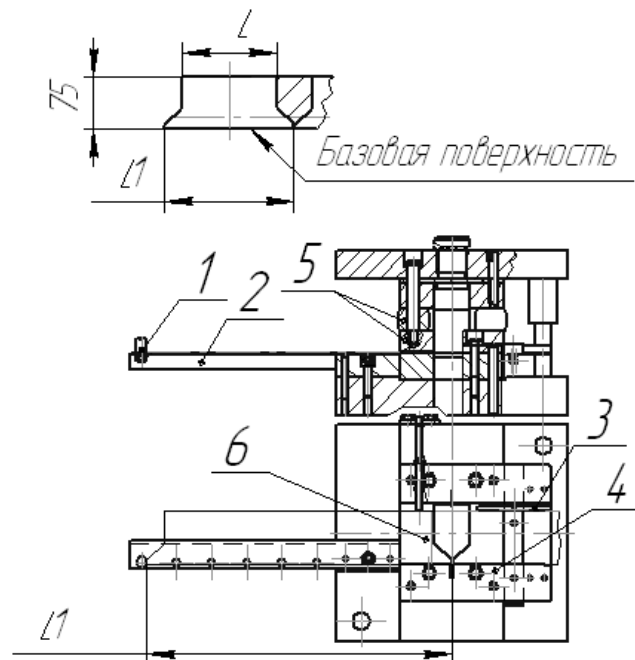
Штамп для резки заготовки детали «стойка» и схема раскроя исходного материала:
